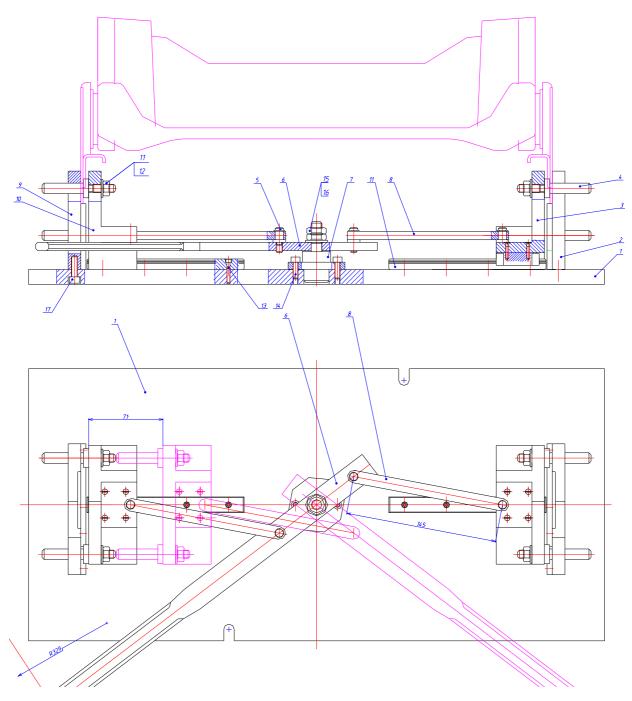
Калибр контроля каркаса спинки сиденья
